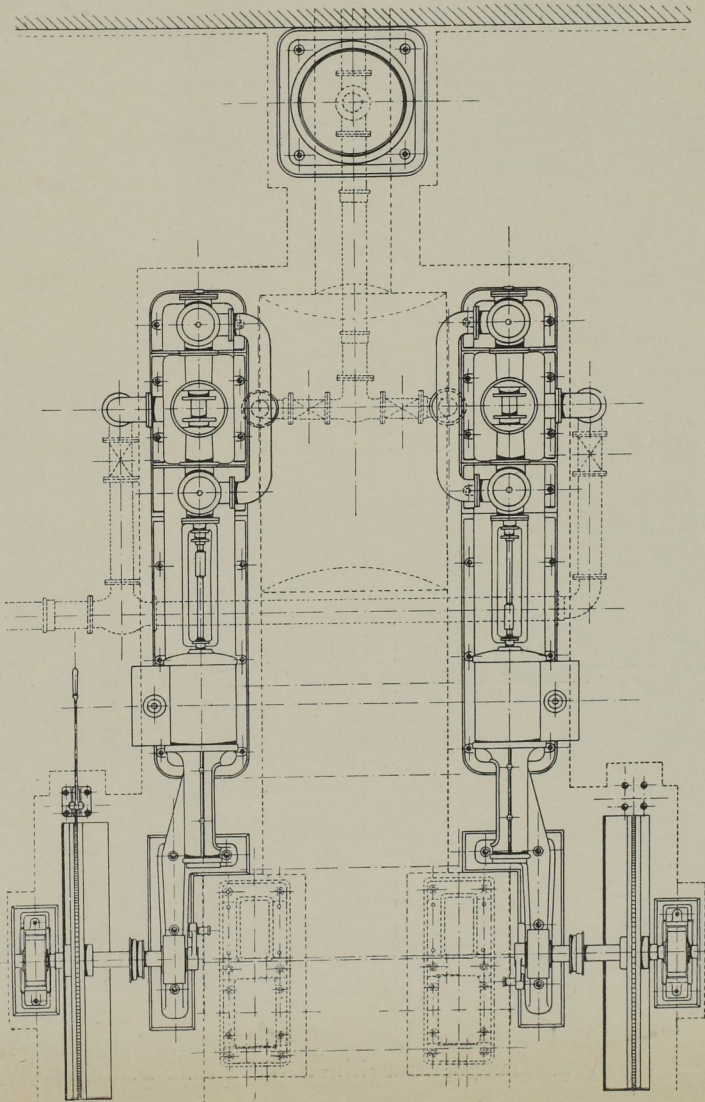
Grundriss der Pumpmaschine. Masst. 1 : 75.
